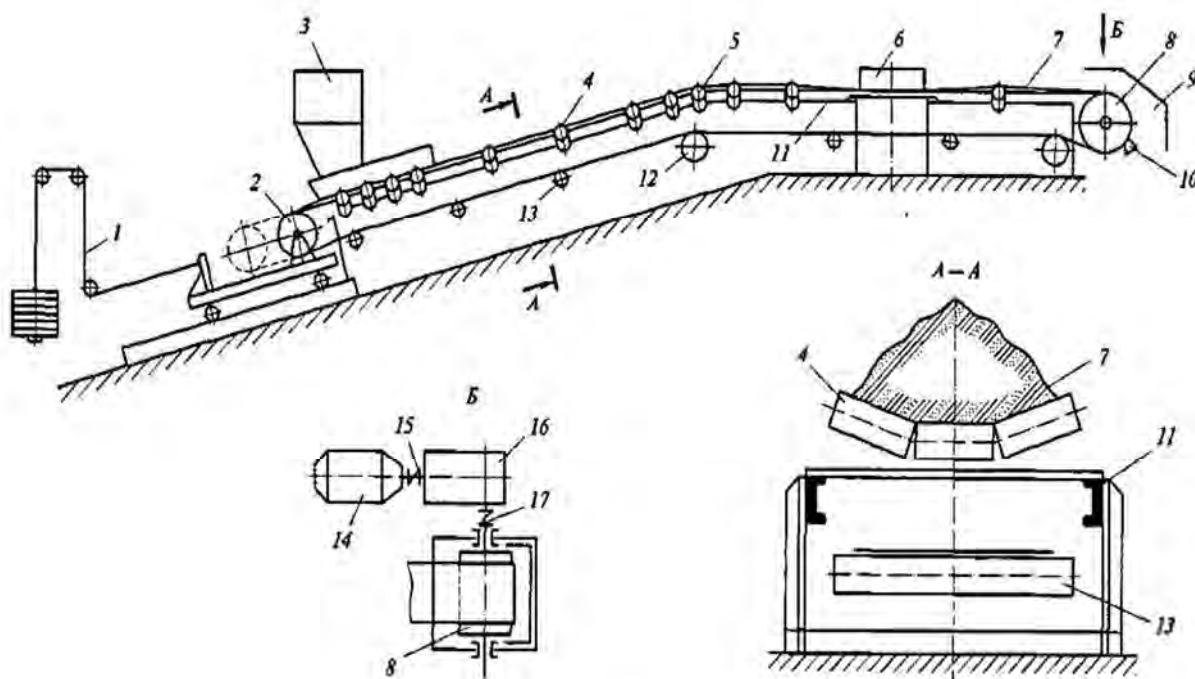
Ленточный конвейер: 1 – натяжное устройство; 2, 8, 12 – натяжной, приводной и отклоняющий барабаны соответственно; 3 – загрузочная воронка; 4, 13 – роликовые опоры; 5 – роликовая батарея; 6 – плужковый сбрасыватель; 7 – лента; 9 – разгрузочная короба; 10 – скребок; 11 – металлоконструкция; 14 – электродвигатель; 15, 17 – муфты; 16 – редуктор
